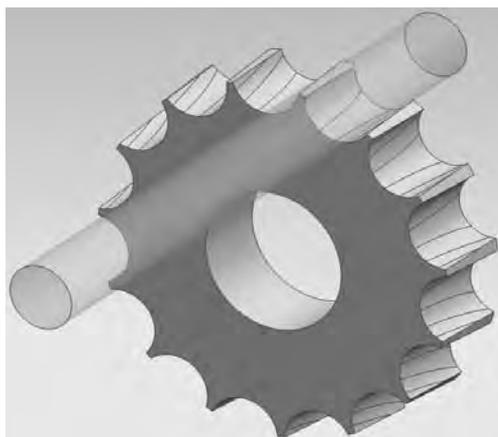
Схема вычитания твердого тела ролика из твердого тела заготовки сателлита
